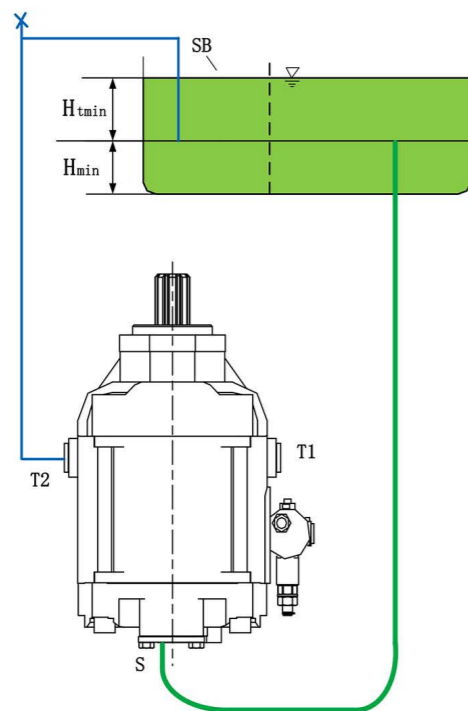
Einbau V60N unter dem Tank (Vertikaler Einbau)
